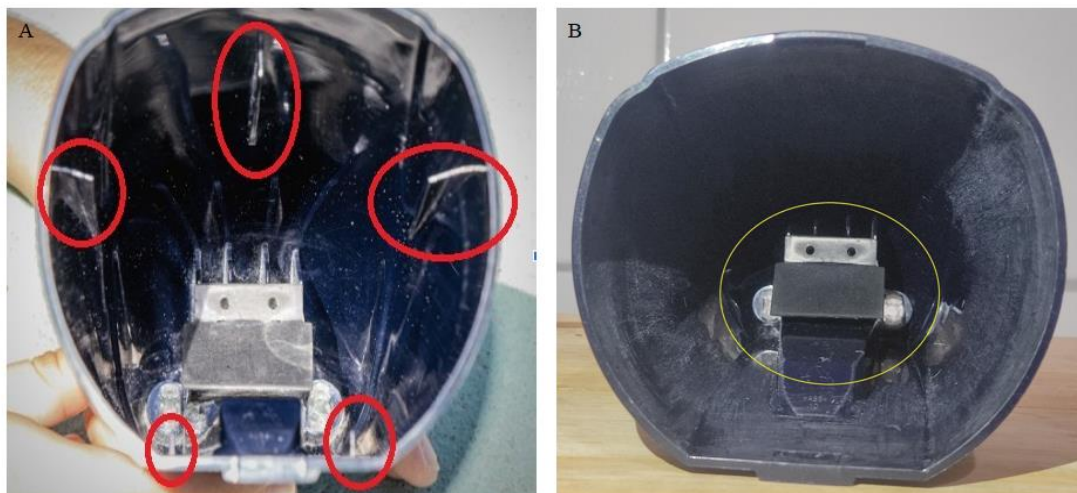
(A) Recipiente de pó com destaque para as hastes que foram removidas; (B) Lacuna do recipiente de pó.
